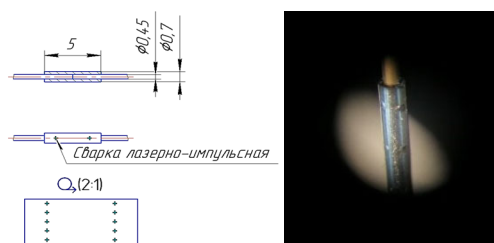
Фото под микроскопом места приварки лазерно-импульсной сваркой нитинола с нитинолом и схемы приваривания
